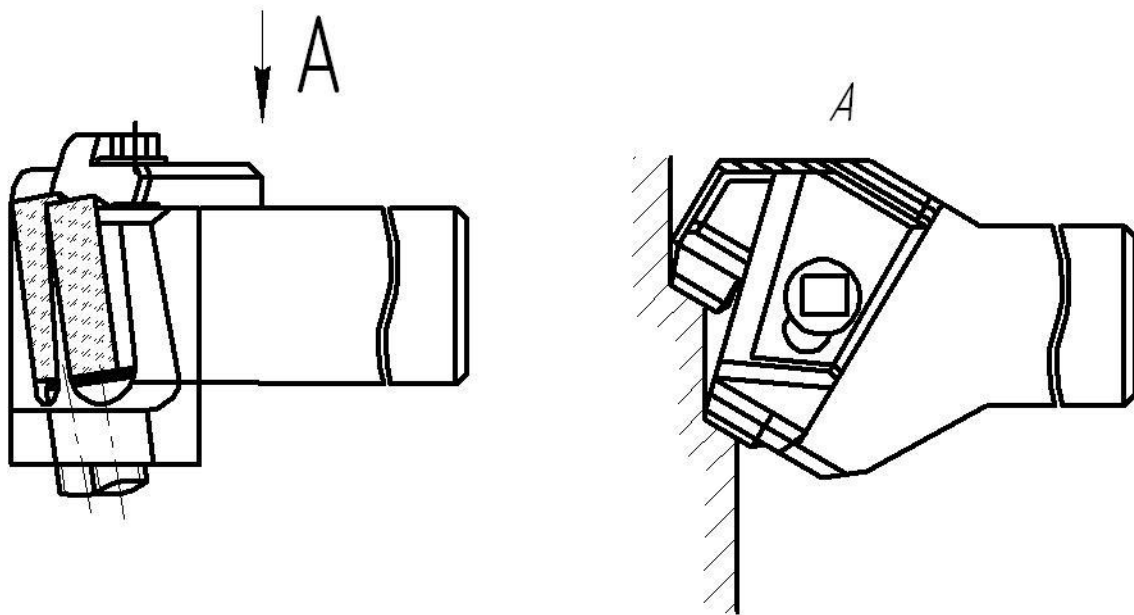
Резец с вертикальным расположением твёрдосплавной пластины
